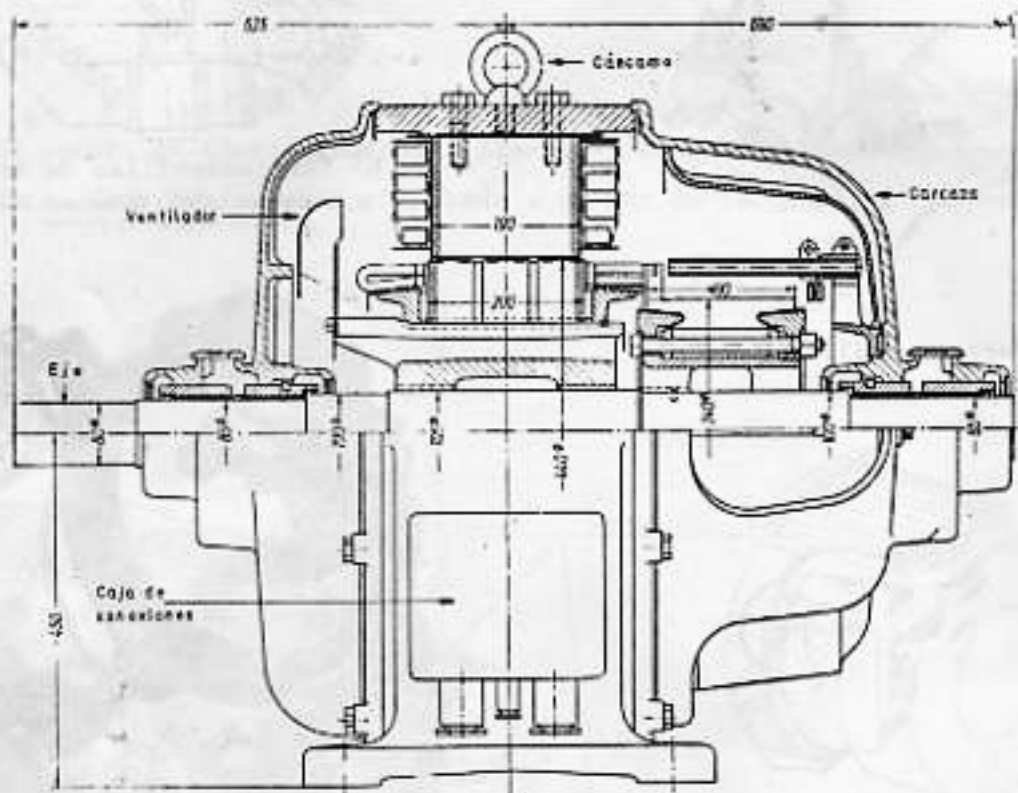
Máquina de C.C. de 100 KW, 240 V, 975 r.p.m., 435 A (B.B.C.). (Dimensiones en mm).
